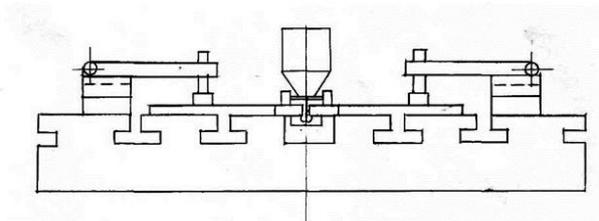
Схема сварки поперечного сварного шва карты
